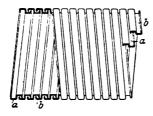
Schlauch mit mehrgängigem Gewinde.
